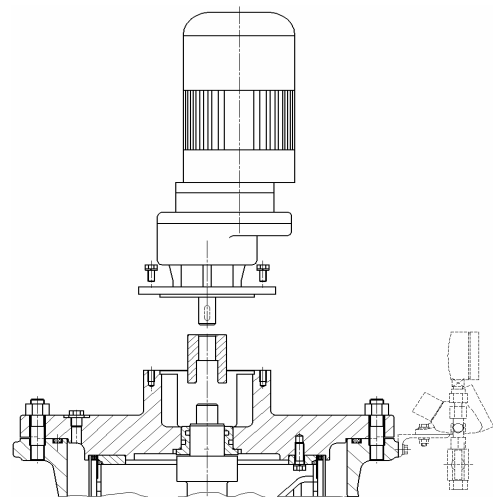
Снятие редукторного двигателя R5-8 DN65-200
